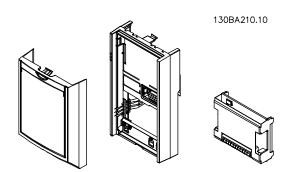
Детали для версий с покрытием/без покрытия
